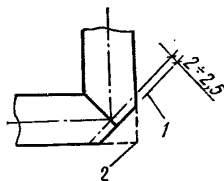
Отрезка вершин угольника при изготовлении тройников и крестовин
